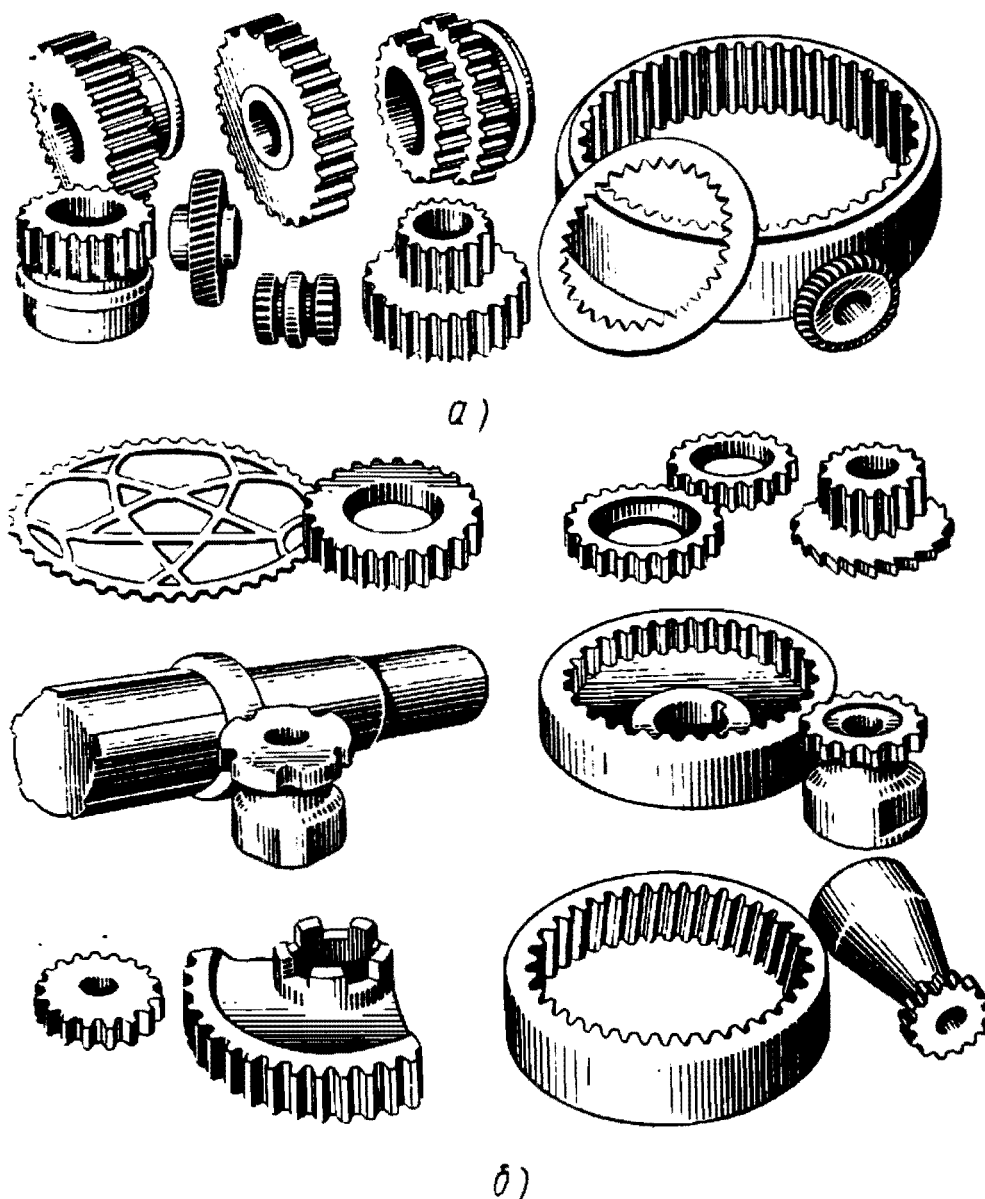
Изделия, изготовляемые на зубодолбежных станках:
